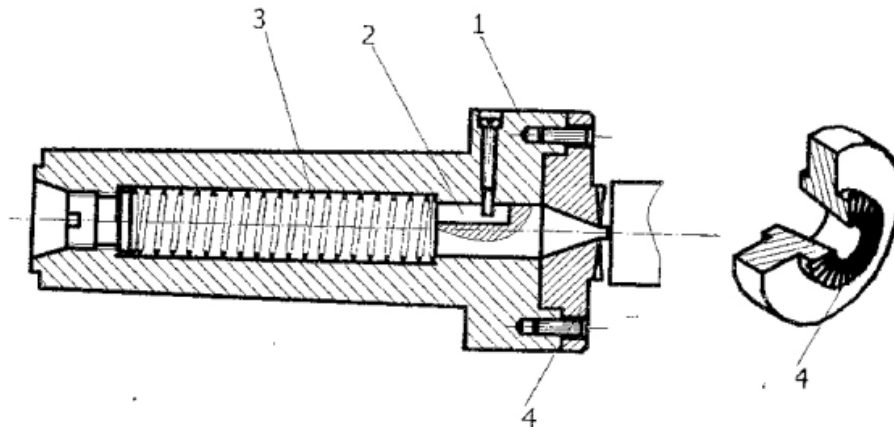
Конструкция поводкового плавающего переднего центра: 1 – корпус; 2 – плавающий центр; 3 – пружина; 4 – сменный зубчатый диск.
